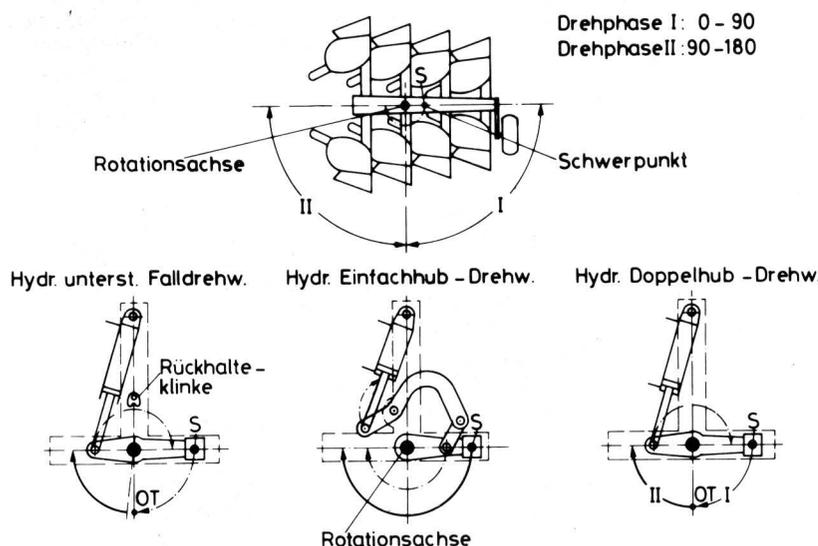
Haupttypen hydraulisch betätigter Pflug-Drehwerke.
